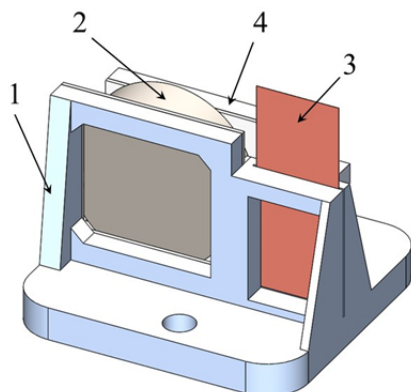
Устройство крепления образцов: 1 – основание; 2 – исследуемый образец; 3 – эталон; 4 – прижим
